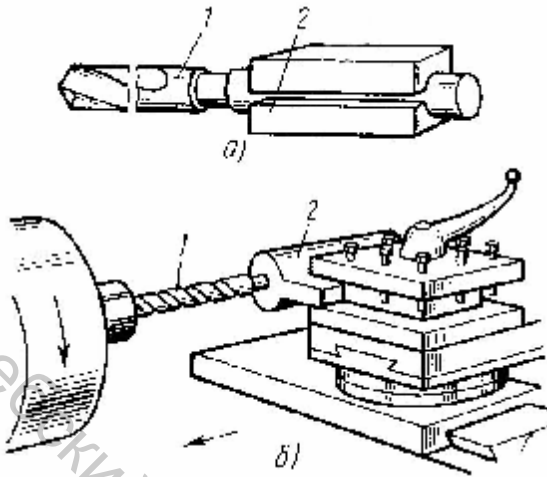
Крепление в резцедержателе сверла с цилиндрическим (а) и коническим (б) хвостовиками
